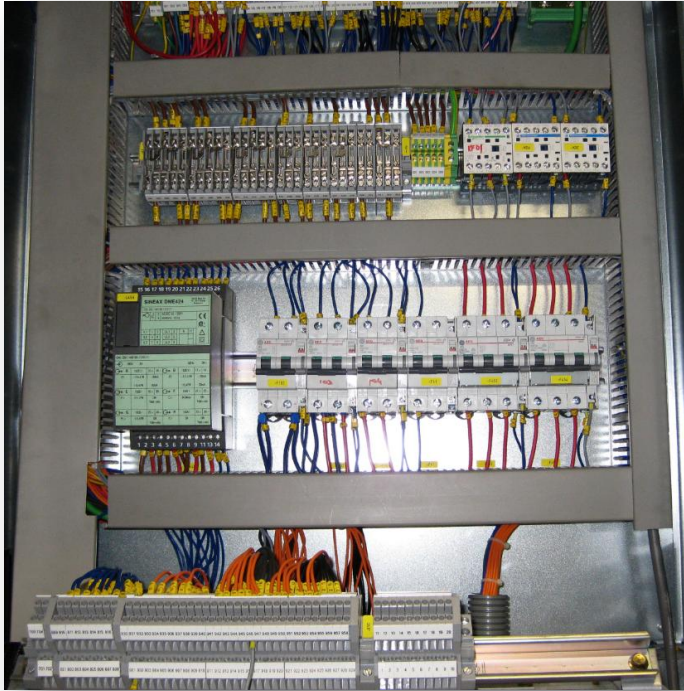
KLEMMENRAIL BEDRADINGSKAST
